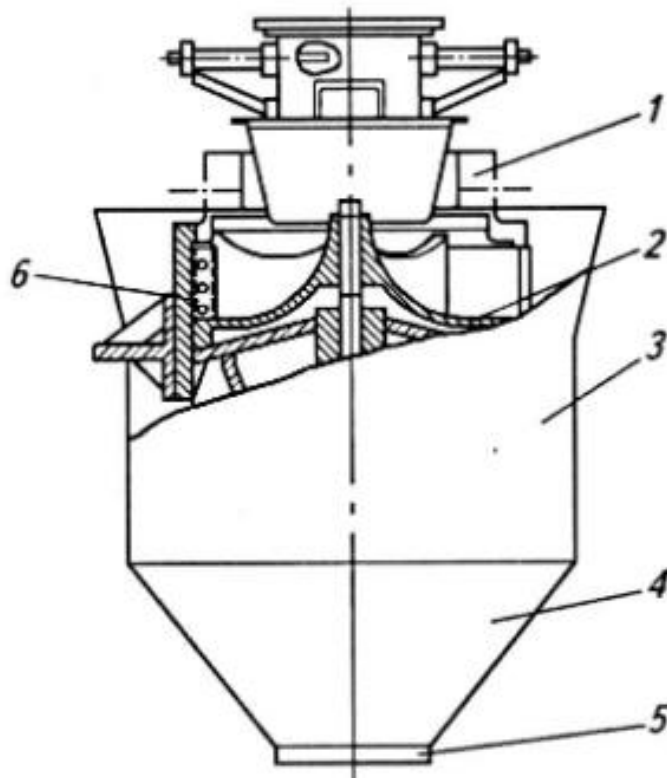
Рамна відцентрована бурякорізка: 1 - завантажувальний бункер; 2 — трилопатевий равлик; 3 - люк; 4 - днище; 5-корпус; 6 ножова рама
